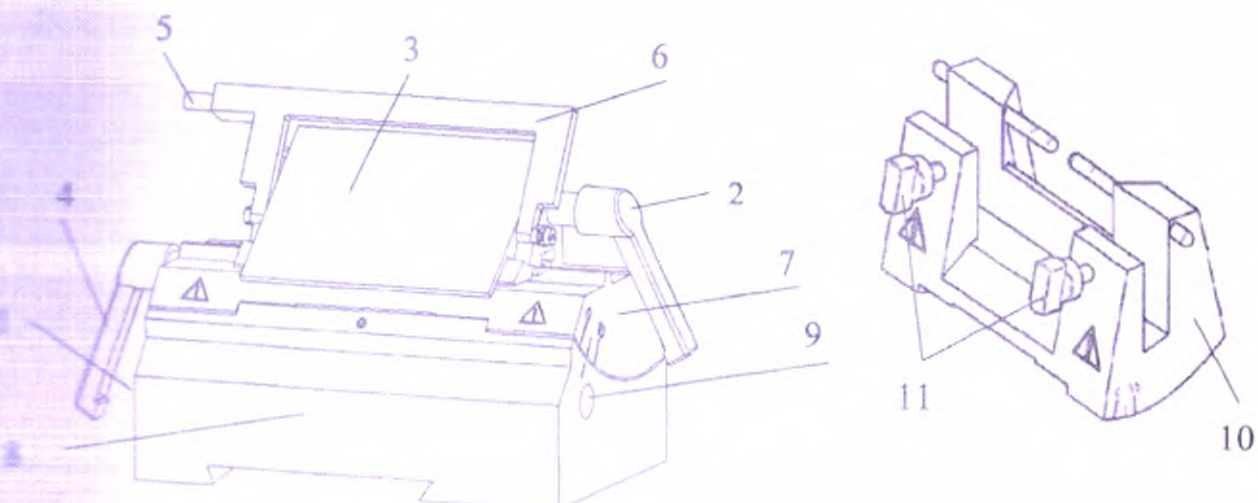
Установка держателя стального ножа, держателя лезвия и его основания
